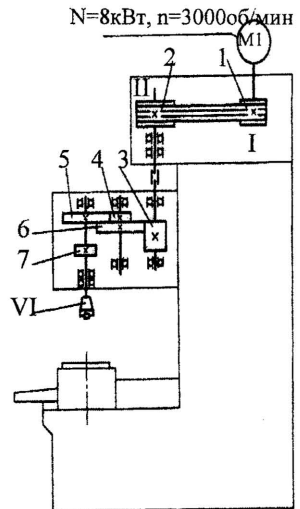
Кинематическая схема главного привода мод. ЛФ-260МФЗ
